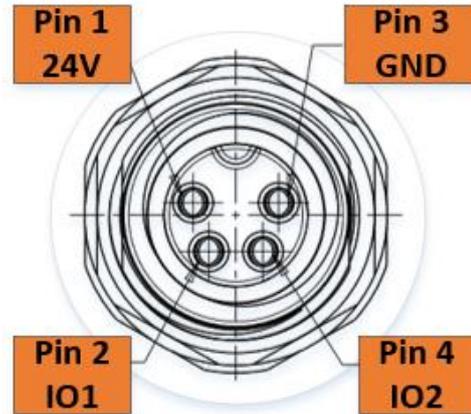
Steckplatzbelegung Werkzeug-E/A
